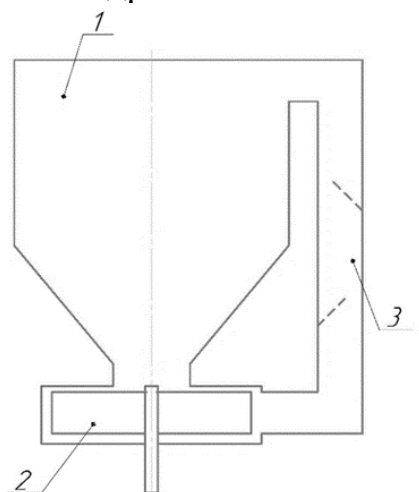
Схема установки для приготовления зерновой патоки с пассивным дезинтегратором в виде перфорированной прямой решетки: 1 – корпус; 2 – насос; 3 – пассивный дезинтегратор
